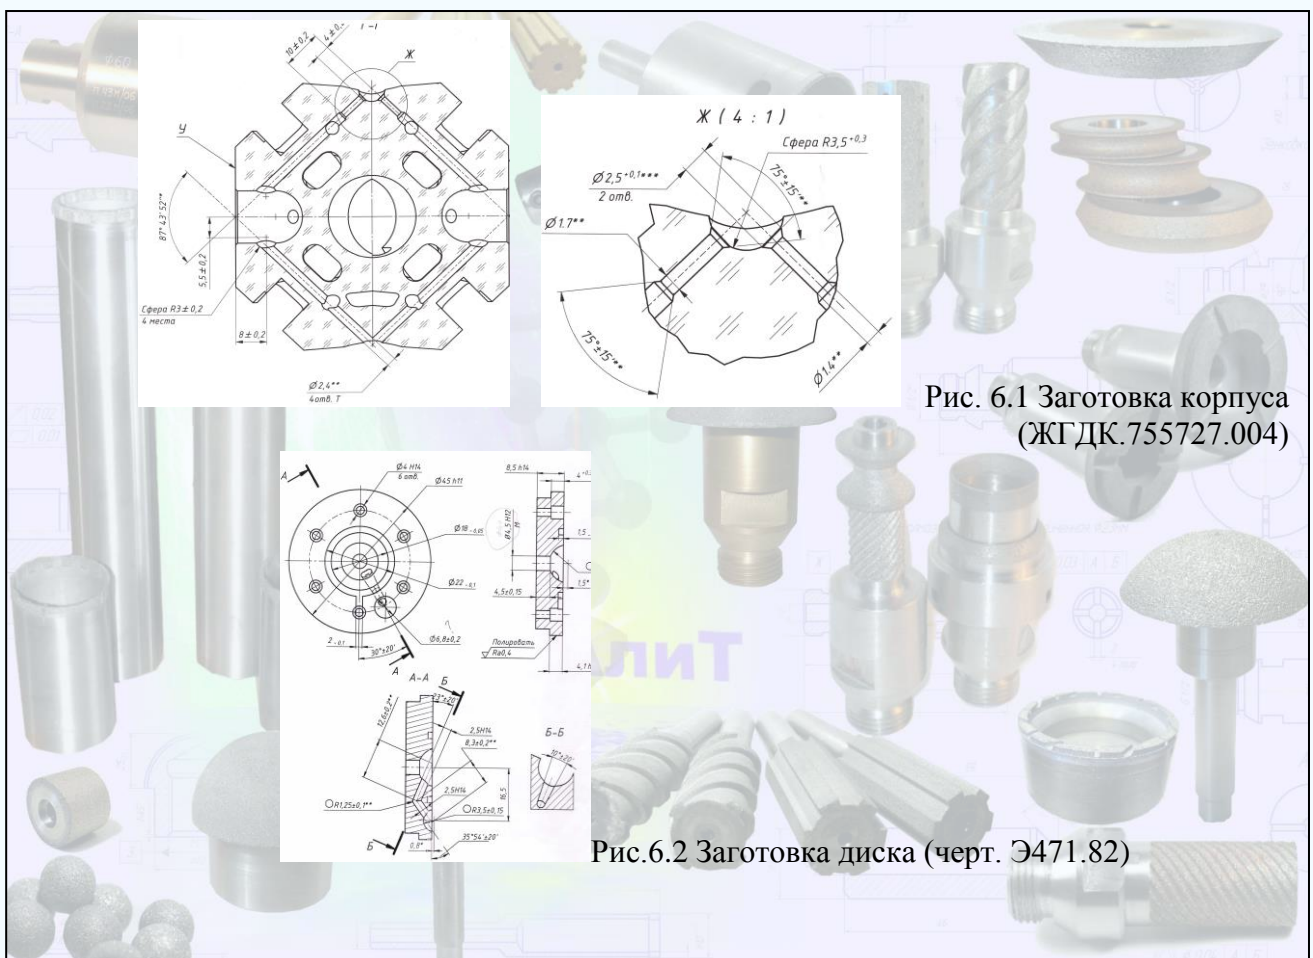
Заготовка корпуса (ЖГДК.755727.004)
